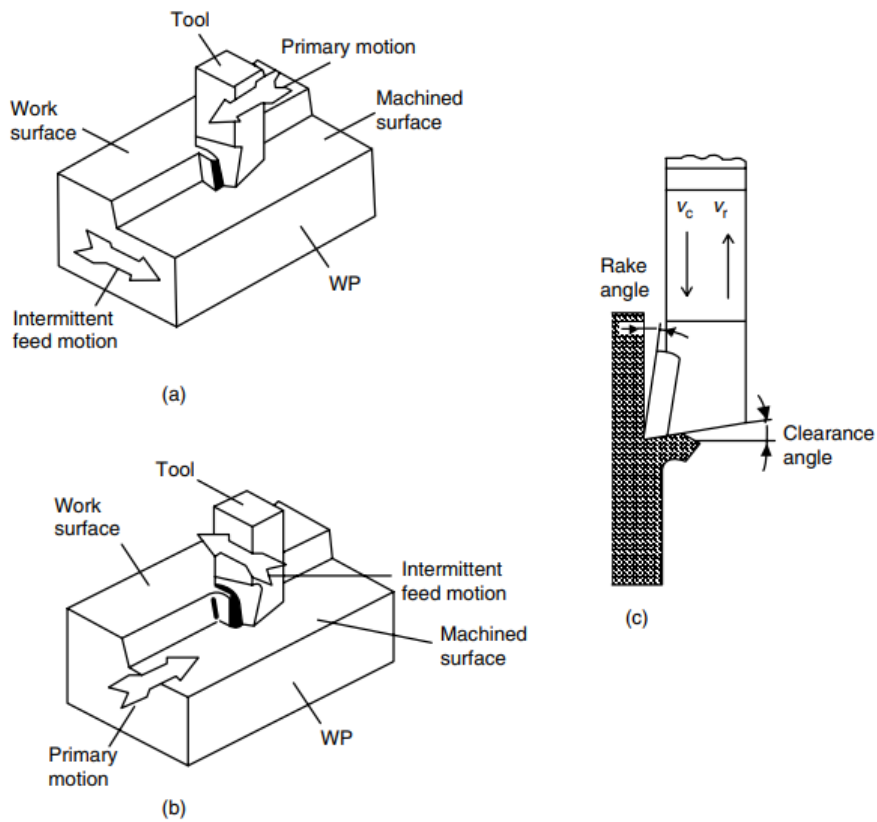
Основні види і рухи процесу довбання [12]
